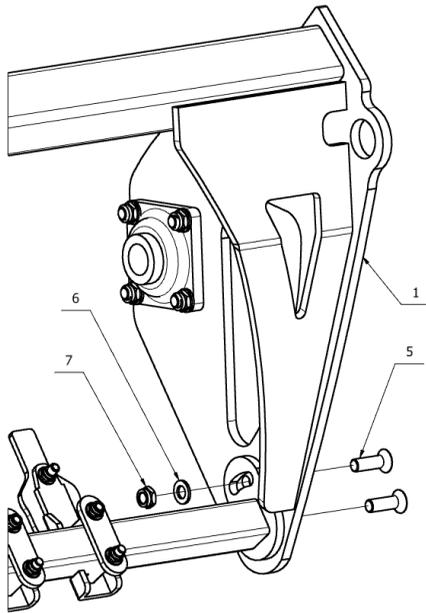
Scheibenwalze Ø600mm – Befestigung des Balkens mit dem Abstreifer.
